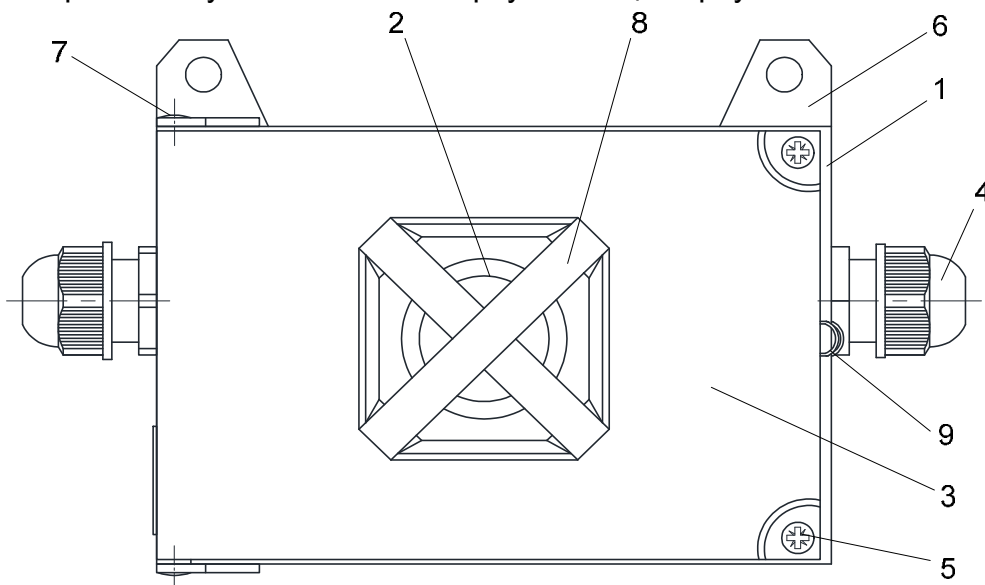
Излучатель светозвуковой искробезопасный СЗИ-И
